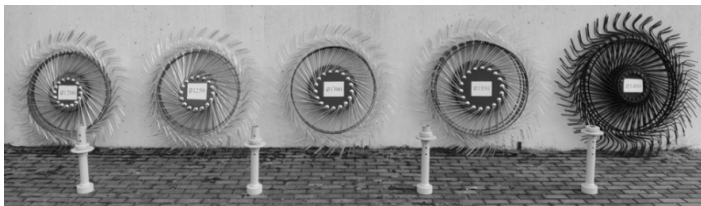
Изготовленные сменные сгребающие колеса макетной установки
